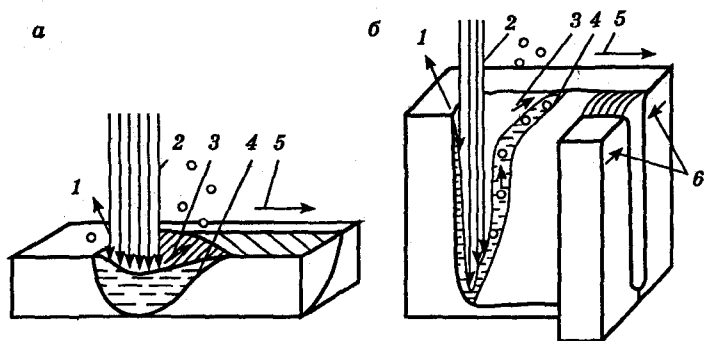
Схема электронно-лучевой сварки металлов малой (а) и большой (б) толщины:
